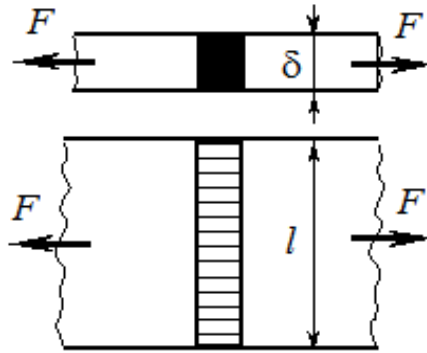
Розрахункова схема зварного стикового з'єднання на міцність
